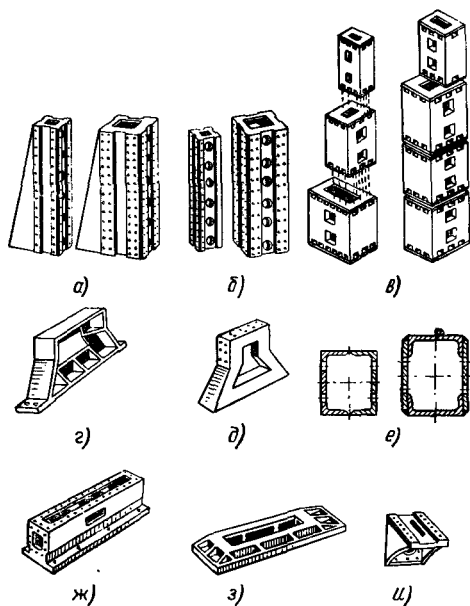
Типовые конструкции несущих элементов каркаса сборочного приспособления
